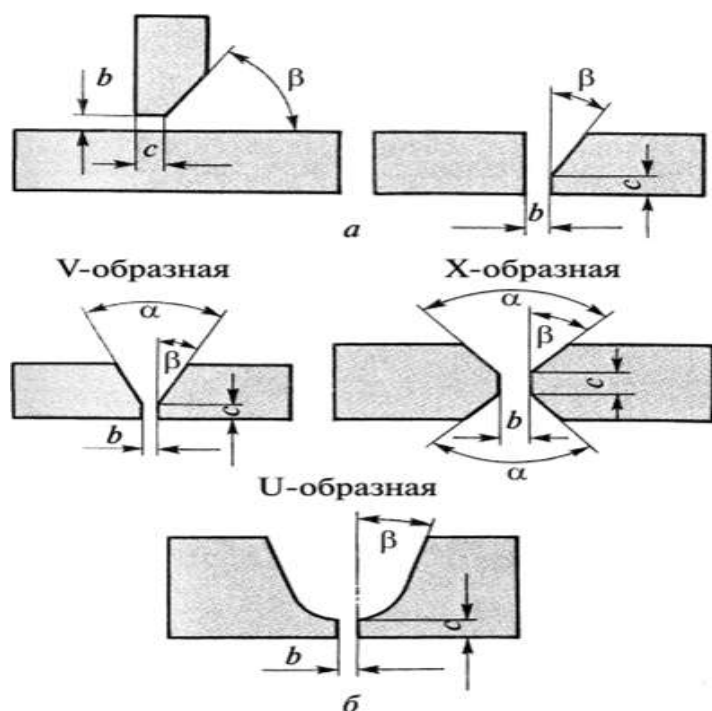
Конструктивные элементы разделки кромок под сварку: *а* — разделка одной кромки; *б* — разделка двух кромок; *в* — зазор; *г* — притупление; *З* — угол скоса кромок; *α* — угол разделки кромок
